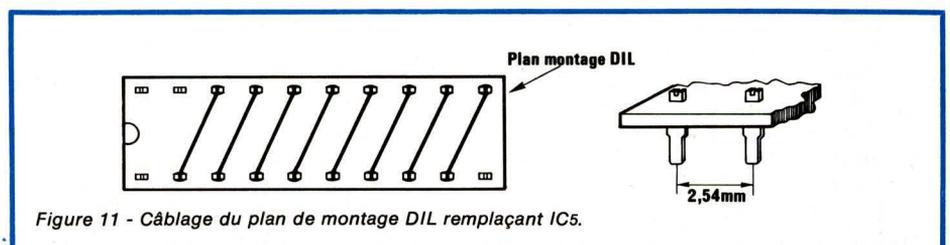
Câblage du plan de montage DIL remplaçant IC5.
